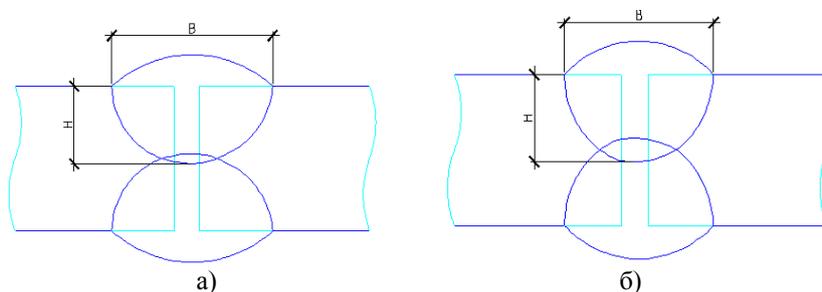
Принципиальная схема проплавления при сварке под флюсами
